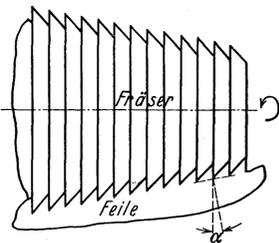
Fräsen der Feilenzähne mit kegeligem Fräser.
